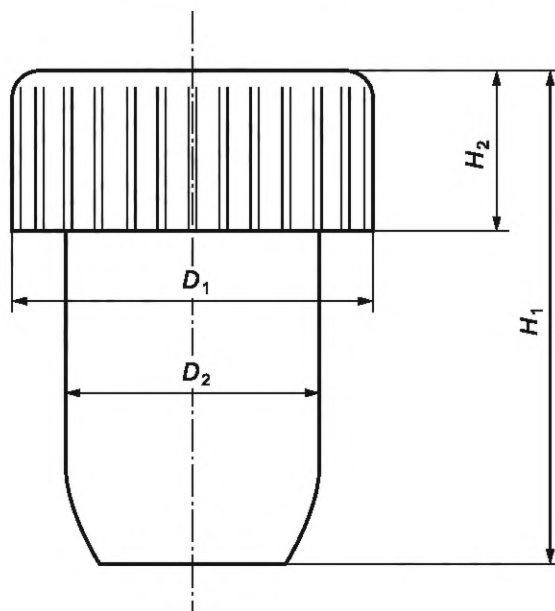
Корковая пробка с дополнительным верхом
